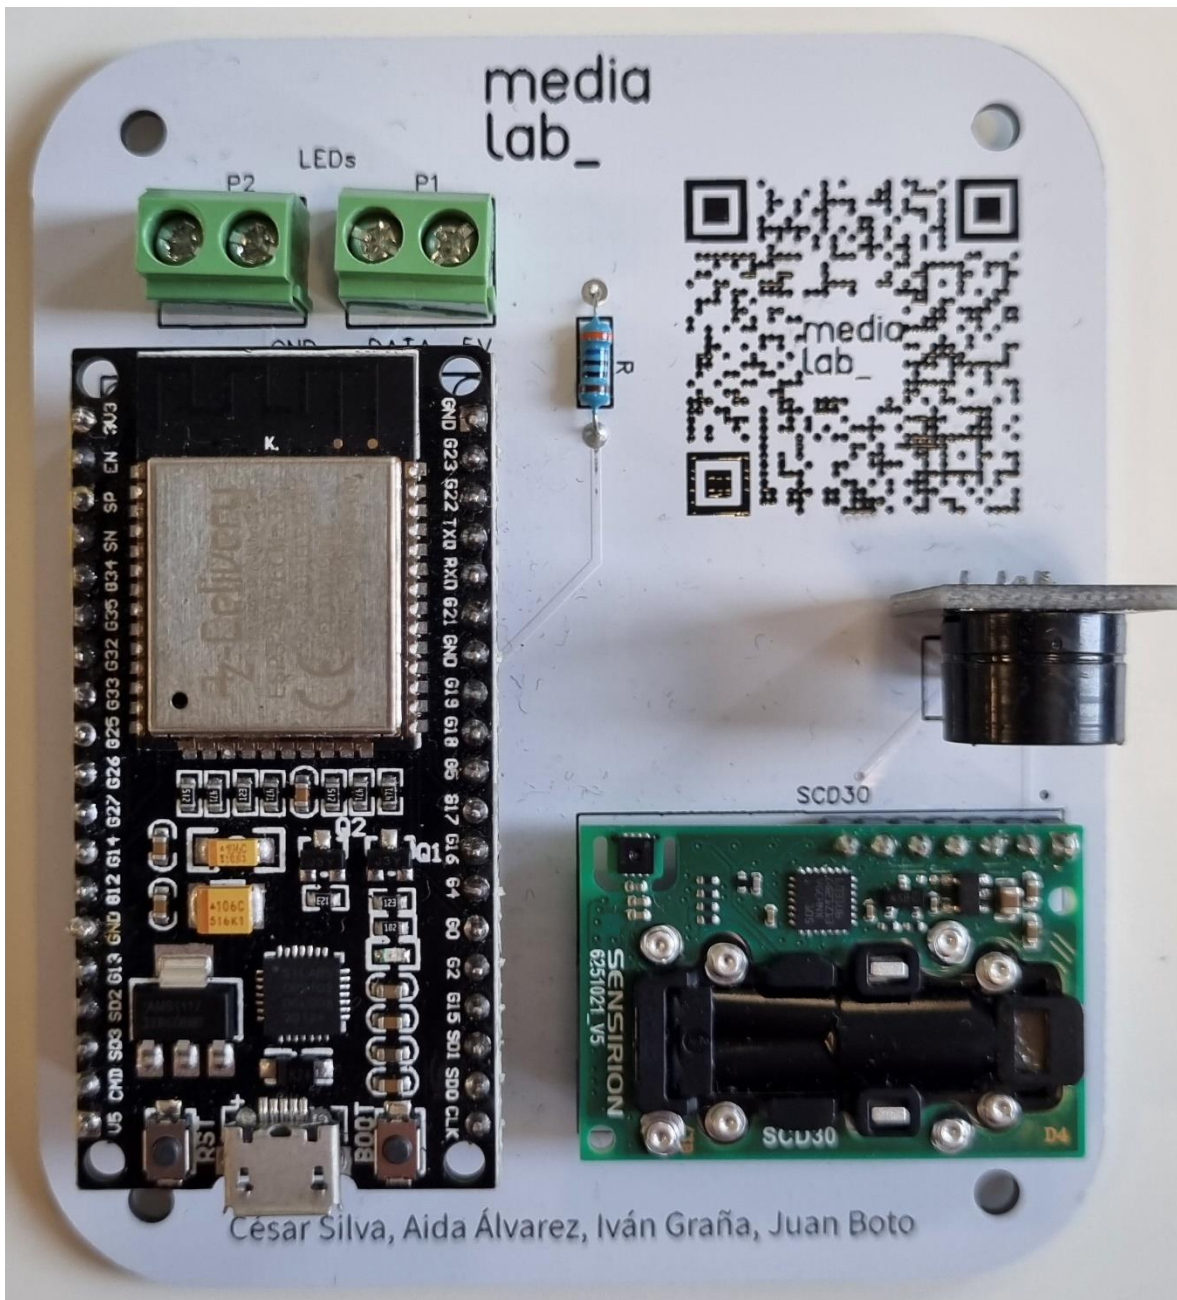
PCB con todos los elementos soldados. Lista para funcionar.
